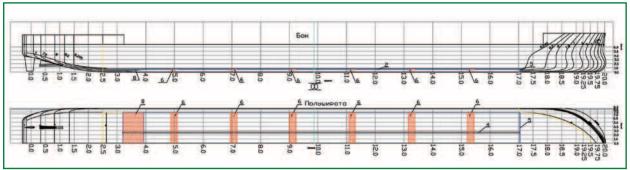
Теоретический чертеж корпуса ССП с энергосберегающим устройством
